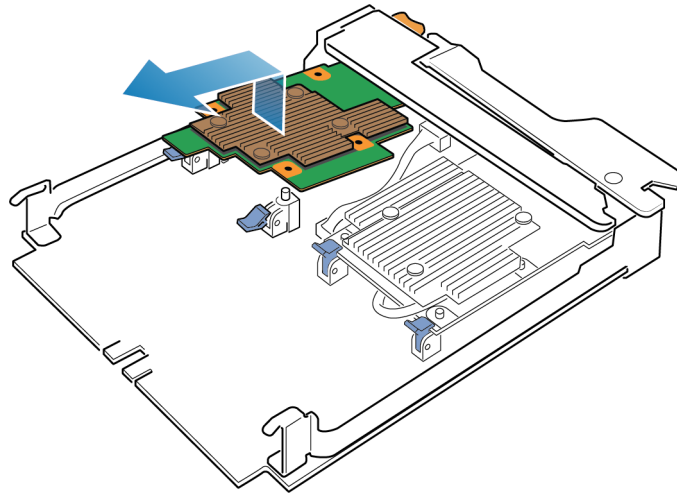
Removendo o Placa de 2 portas de 100 GbE
